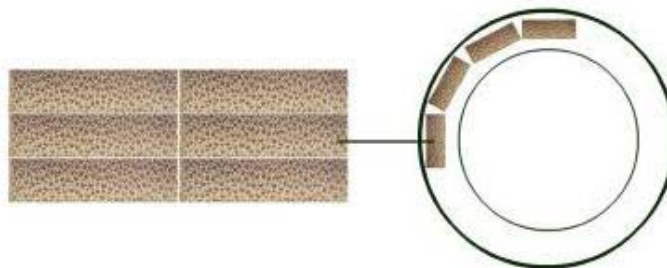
Esquema de retirada das ripas observado da seção transversal.
